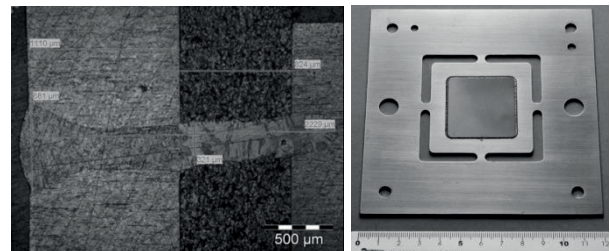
Links: Durchschweißung einer Sintermetallfritte. Schweißnaht vakuumgetestet. Rechts: Plane Integration eines 1 mm dicken Sintermetalls in einen Blechrahmen (ferritischer Edelstahl Crofer 22APU).
